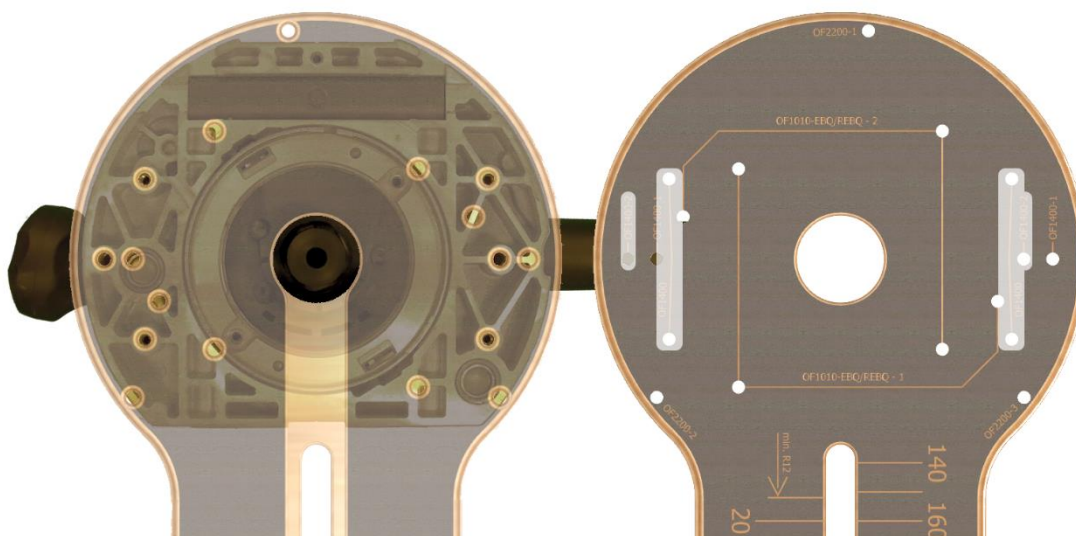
Trous de montage 2 adaptés à Festool OF1400
